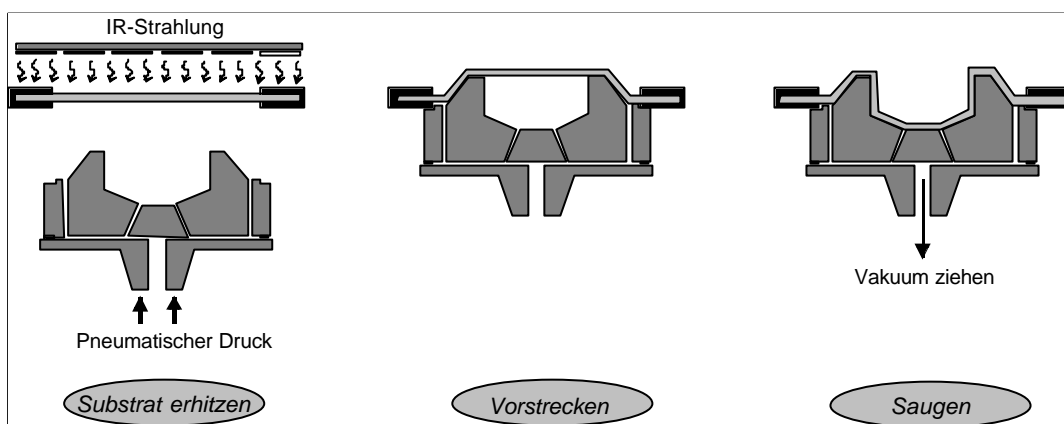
Saugen auf ein Positiv-Werkzeug mit mechanischem Vorstrecken
